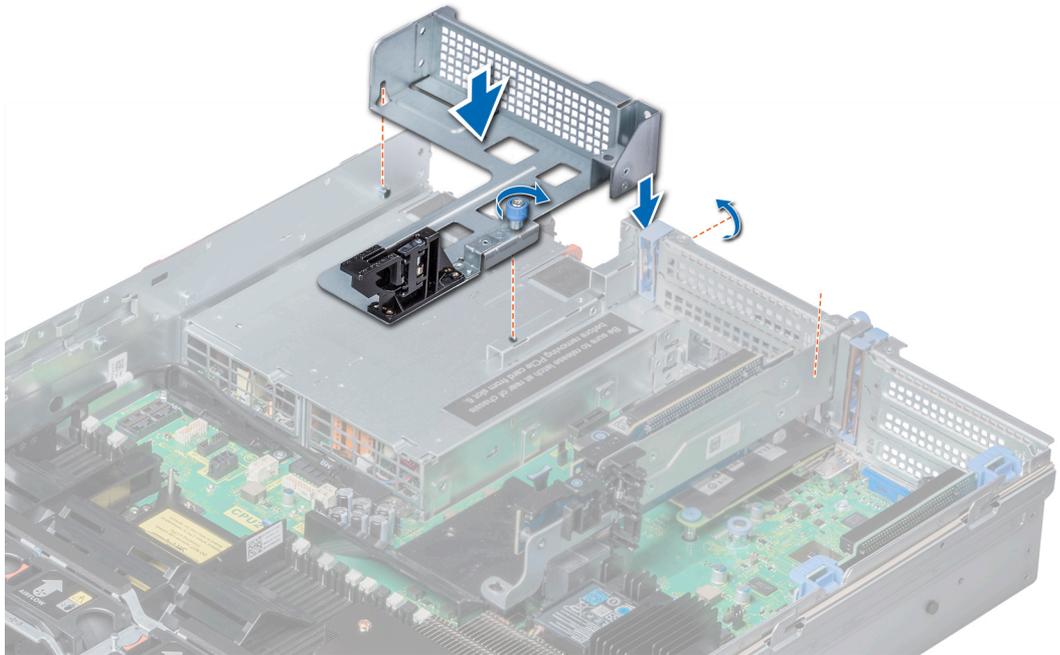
Einsetzen des Platzhalters für Riser 3
